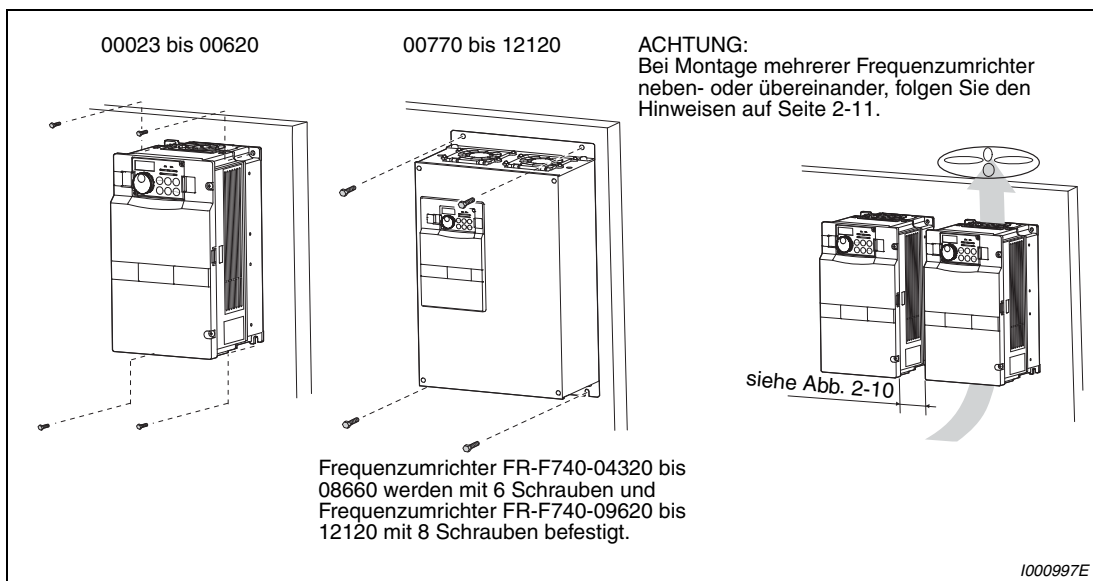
Installation auf der Montageplatte eines Schaltschranks
